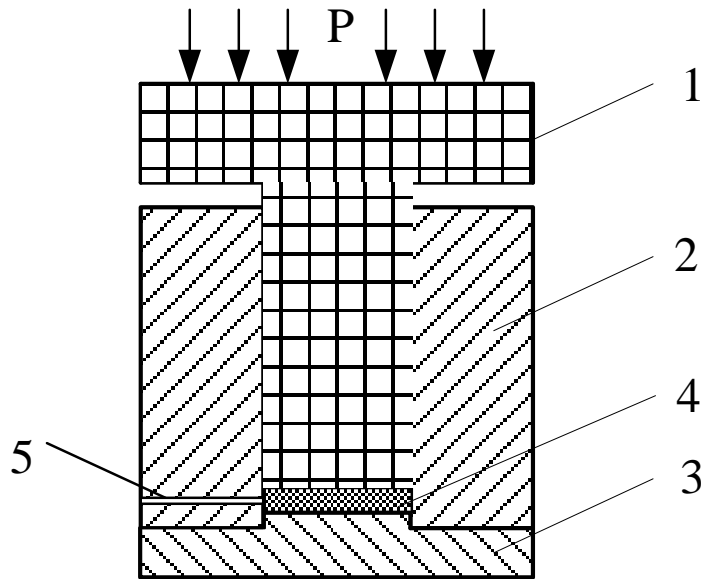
Вид пристрою для формування гранули за умови високого тиску: 1 – поршень; 2 – матриця; 3 – основа; 4 – композиція; 5 – дренажний отвір
